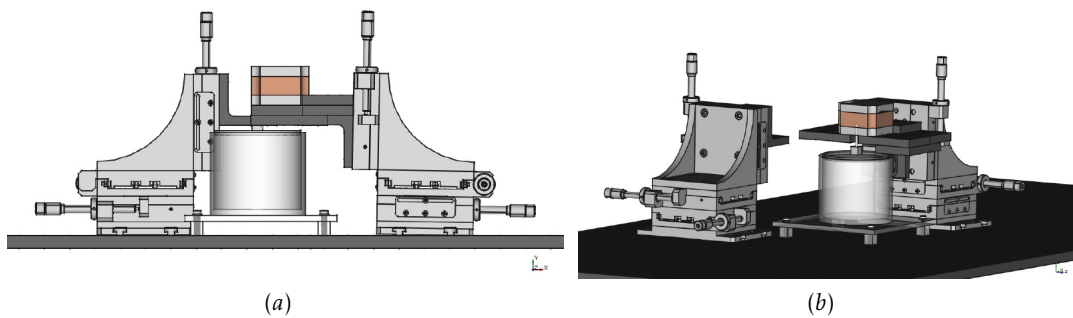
Diseño del montaje experimental: (a) vista frontal y (b) vista isométrica.
